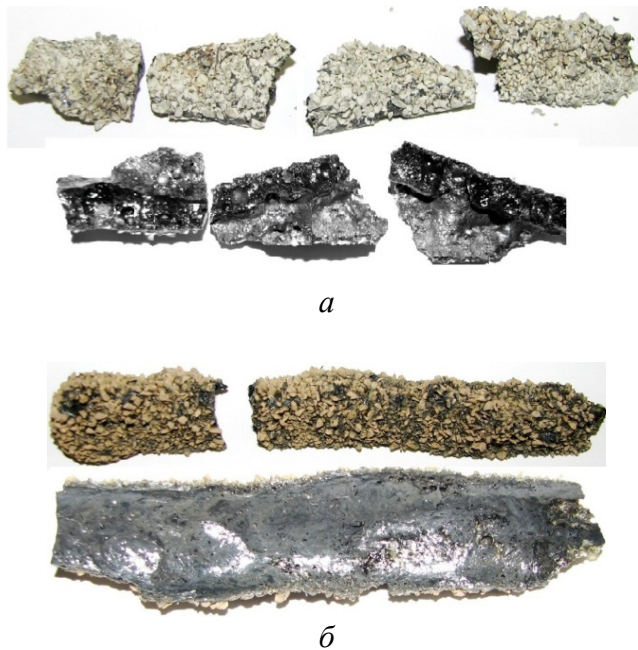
Внешняя и внутренняя поверхности сварочной корки после сварки под слоем флюса ($\times 2$): *а* – шлак габбро-диабазы; *б* – шлак горнблендита
